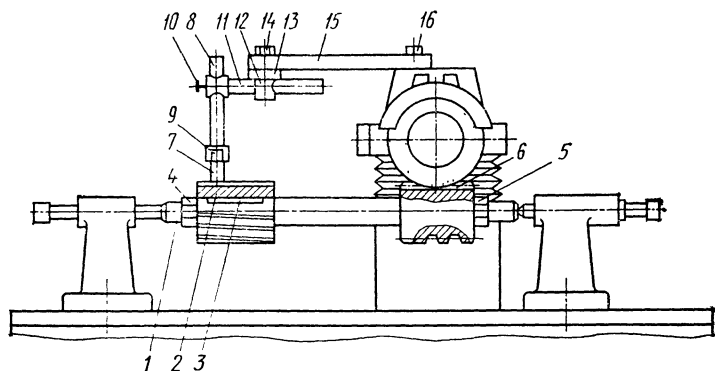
Приспособление для заточки червячных фрез с копиром.
